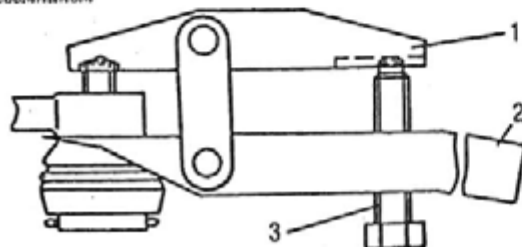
Выпрессовка пальца шарового шарнира из поворотных рычагов и бобышек тяги сошки съемником 7823-6899:
